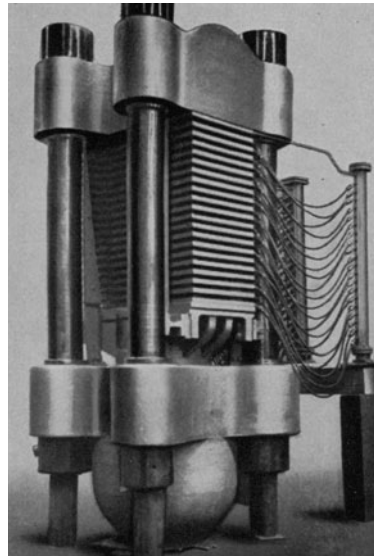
Hydraulische Plattenpresse mit 20 Fächern.
